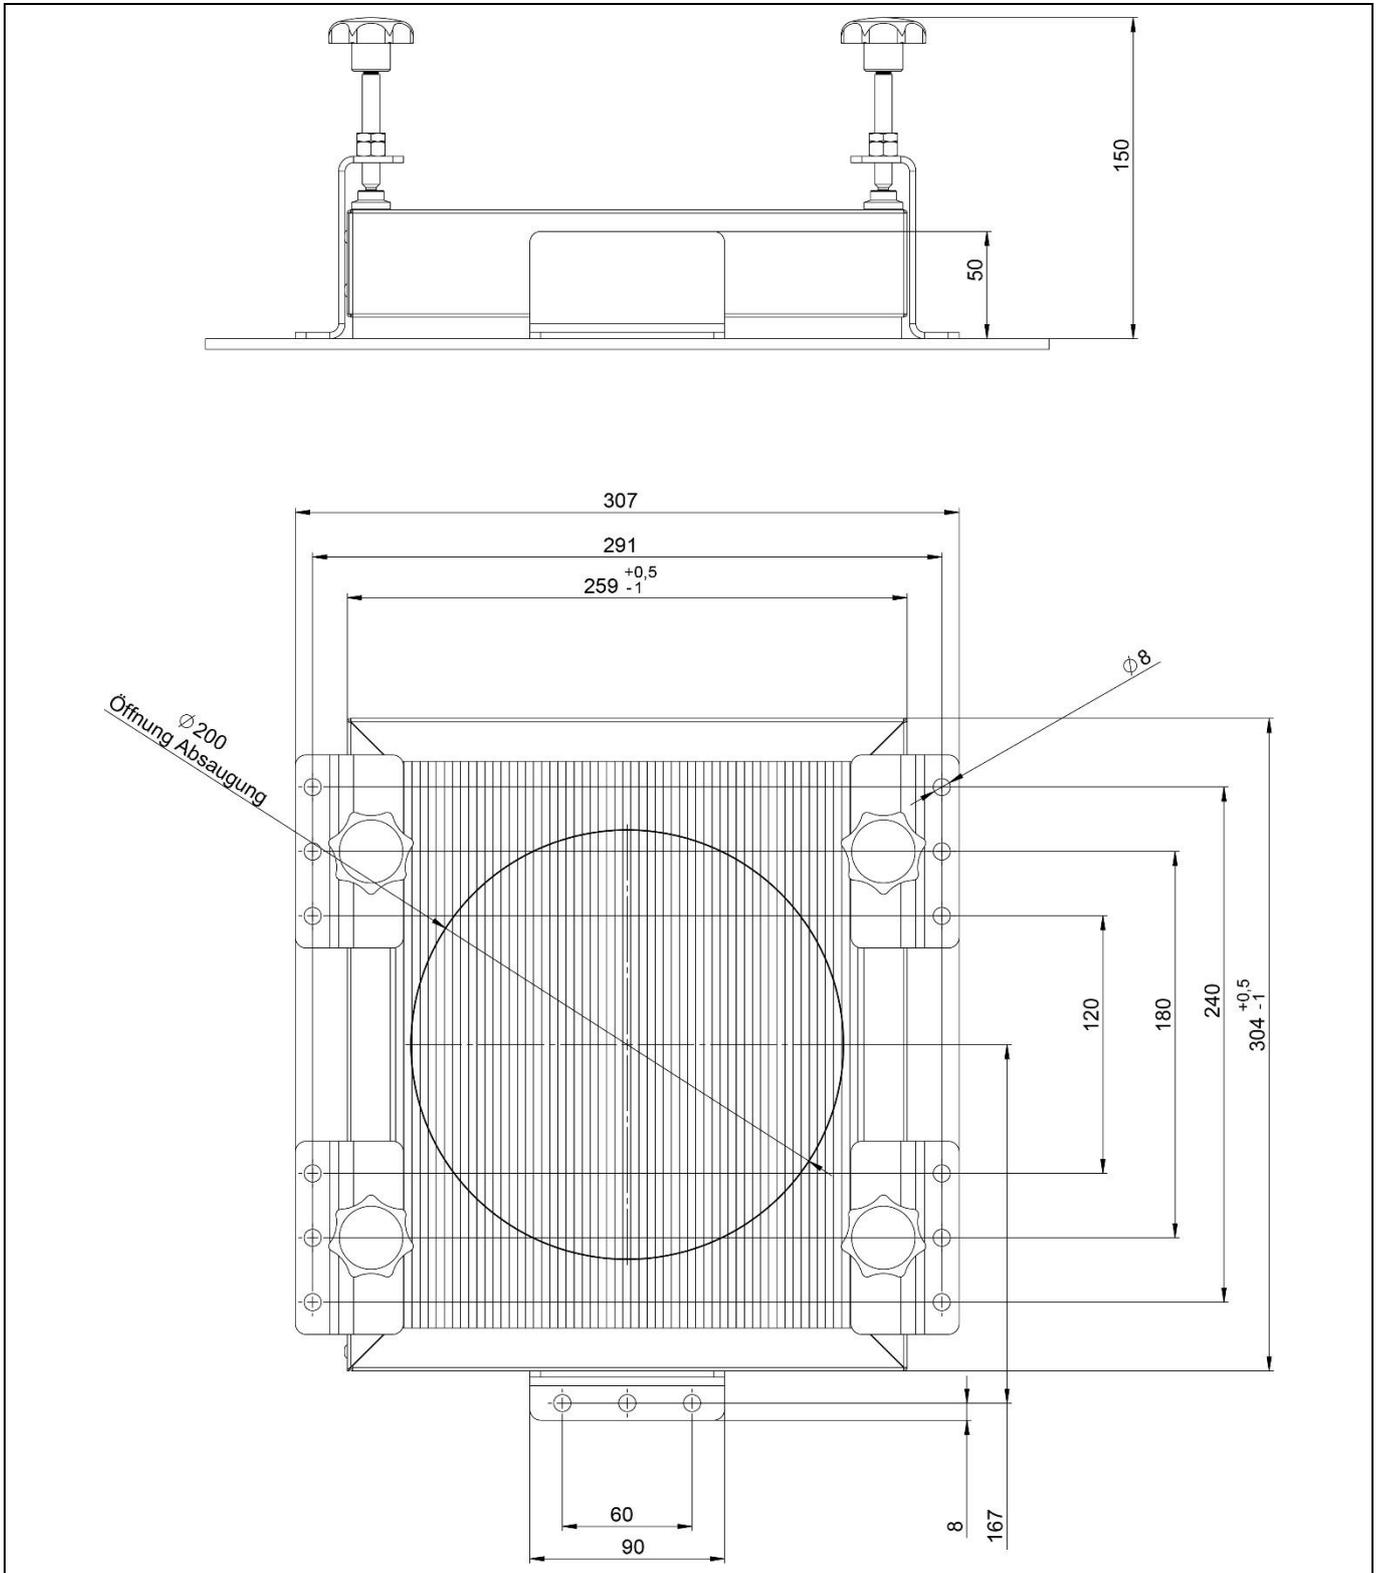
Einbau einer Filterplatte in eine Bearbeitungsmaschine
